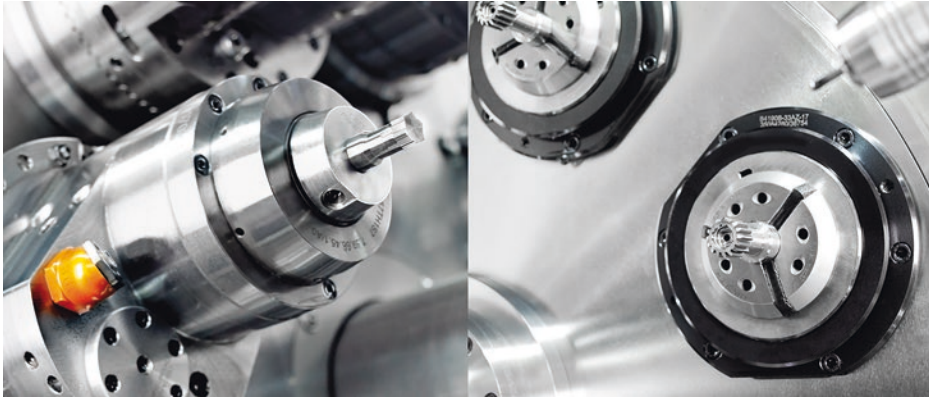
Profilstoßeinrichtung mit Werkzeug (links) und Werkstück mit stirnseitigem Innenprofil (rechts). [Quelle: Schütte]
